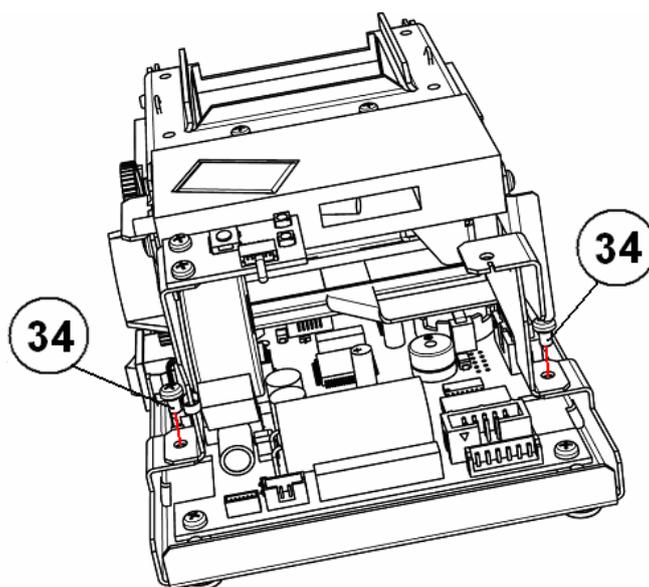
Винты крепления печатающего механизма к шасси.
